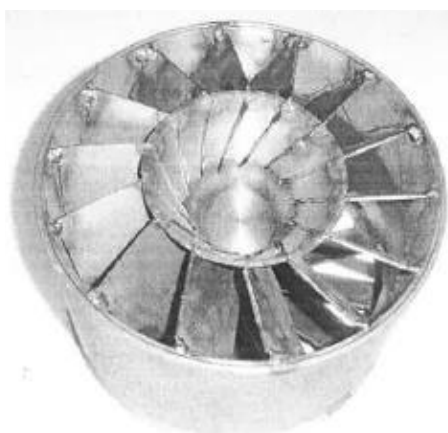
Общий вид воздушный форсунки стабилизатора
